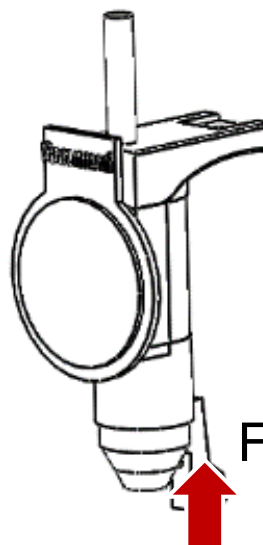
Dispensador en posición inicial diseñado en Solidworks
